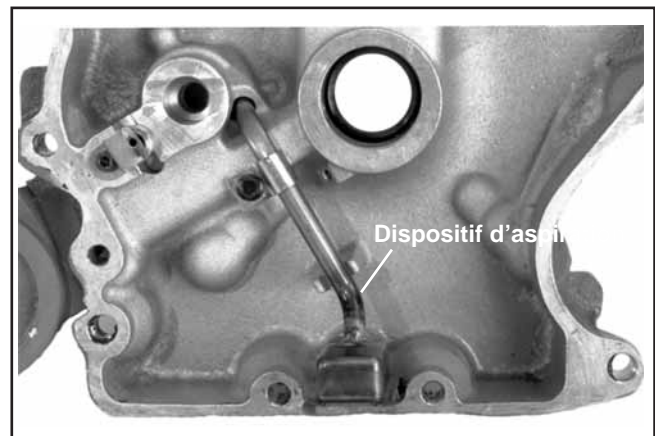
Dépose du joint d'huile et du dispositif d'aspiration d'huile.
